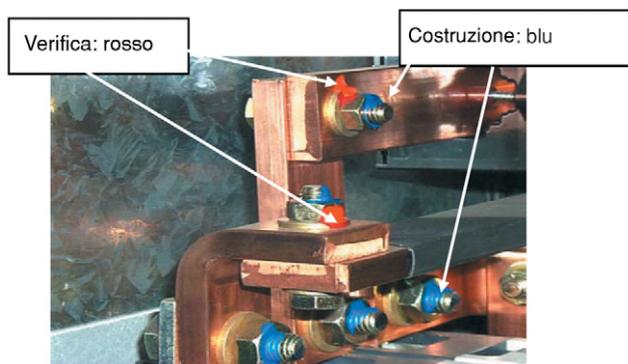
Contrassegno di collegamenti di viti con momenti di serraggio
